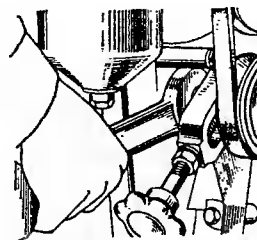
Отвертывание гайки крепления оси шкива
